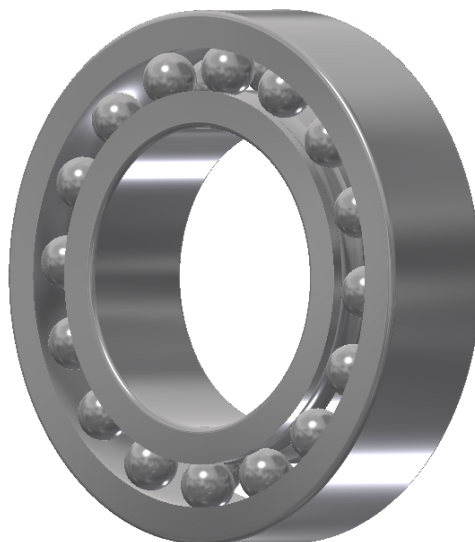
Rodamientos de bolas autoalineados, doble fila, con junta y taladro cilíndrico.
